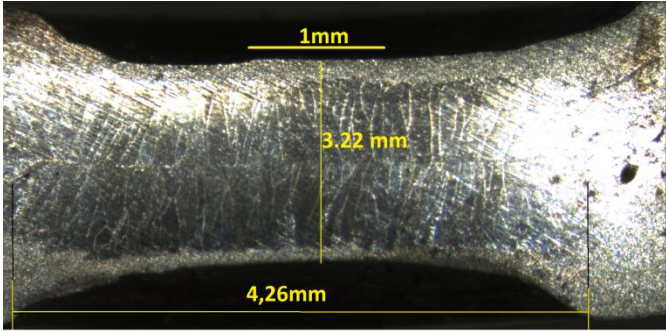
Vue macroscopique d'une coupe transversale du point de soudure
